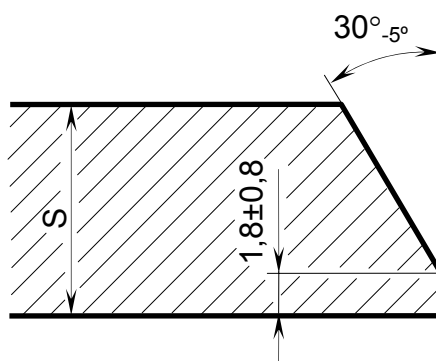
Геометрические параметры разделки кромок торцев труб для ручной дуговой сварки покрытыми электродами после разделительной резки и механической обработки
